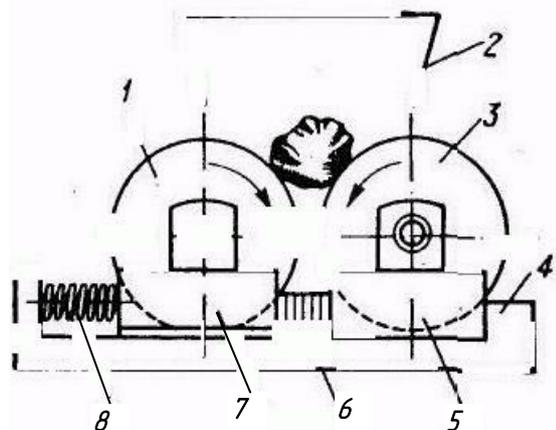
Схема действия двухвалковой дробилки: 1, 3 – валки; 2 – загрузочная воронка; 4 – станина; 5, 7 – подшипники; 6 – прокладка; 8 – пружина
